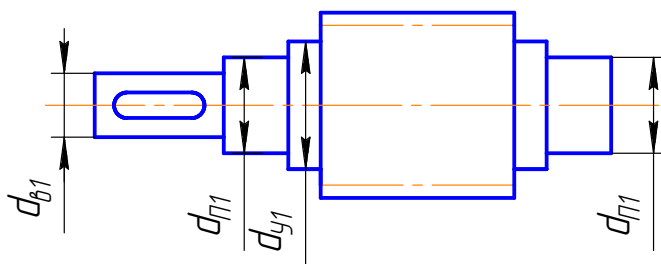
Типовая конструкция быстроходного вала редуктора
